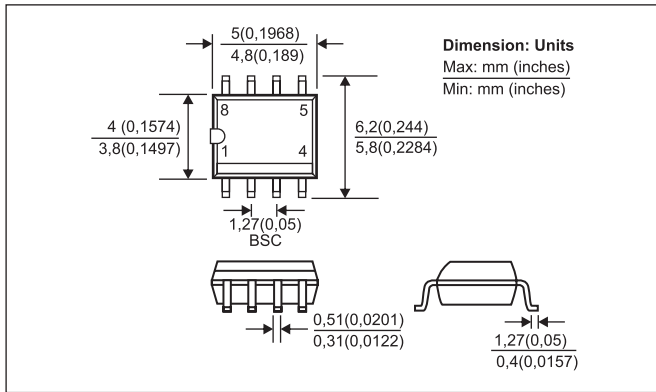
Чертеж с размерами корпуса (типичный вариант)
